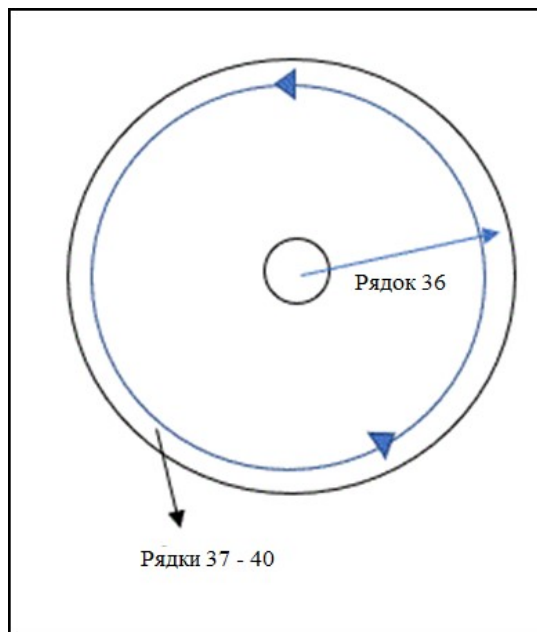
Вид на роботу інструмента всередині циліндра
